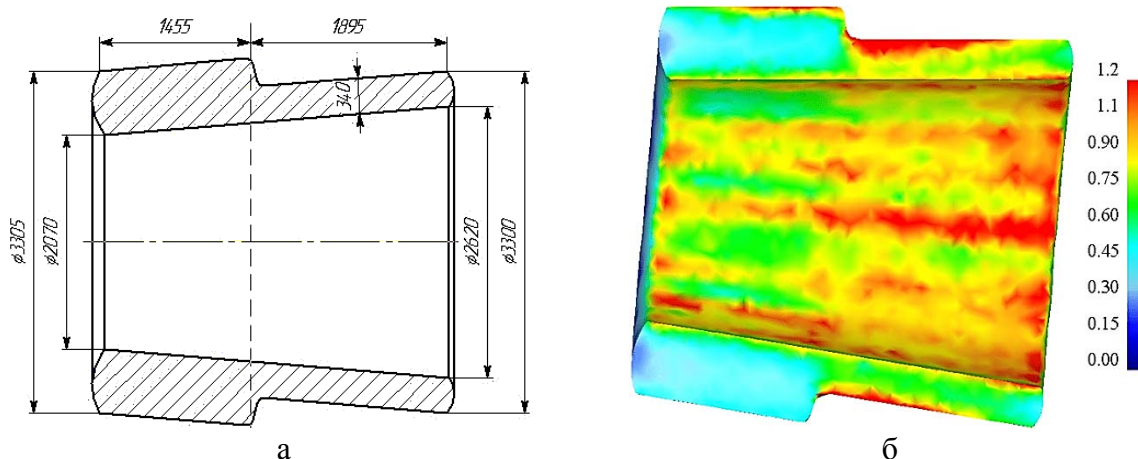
Ескіз (а) та деформований стан поковки після розкочування (б)
